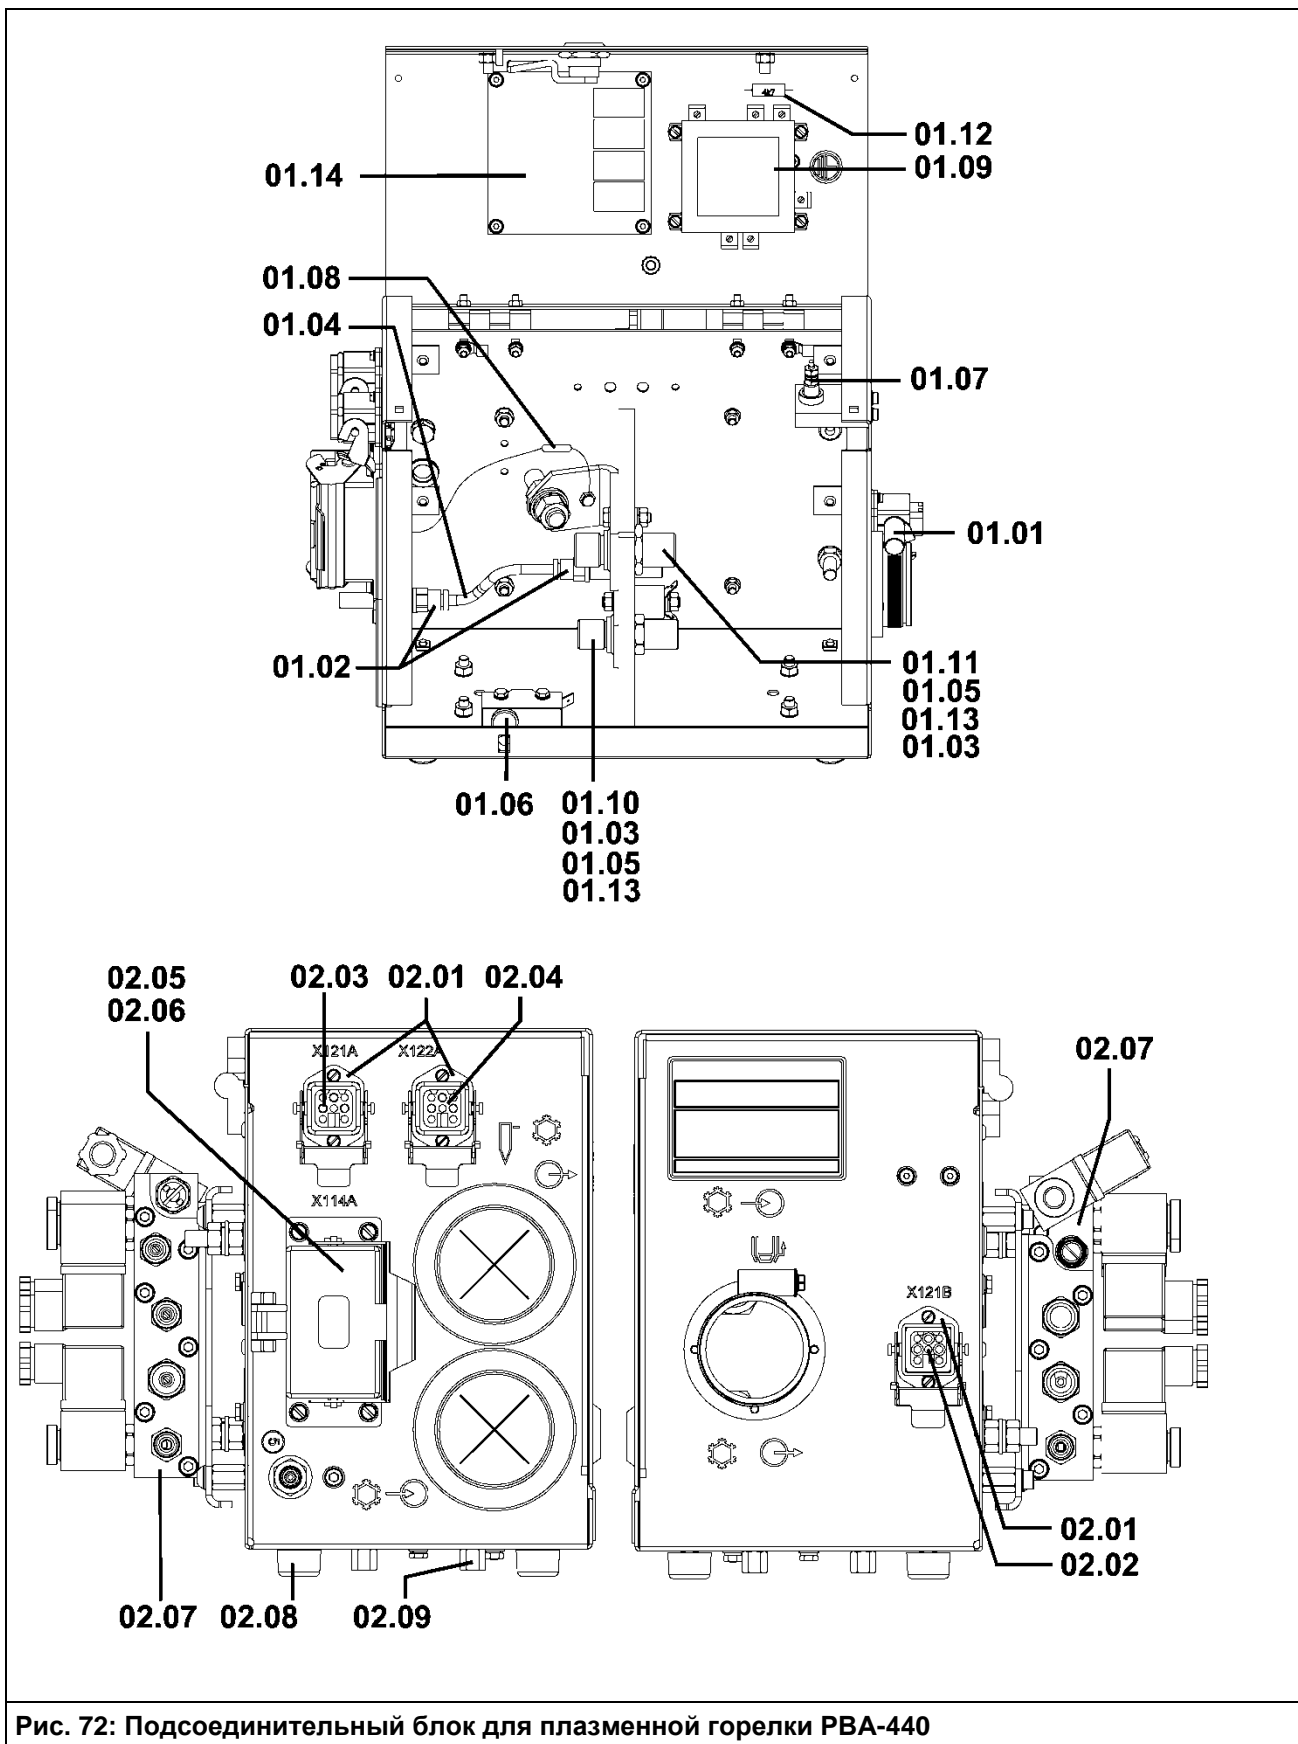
Подсоединительный блок для плазменной горелки РВА-440
